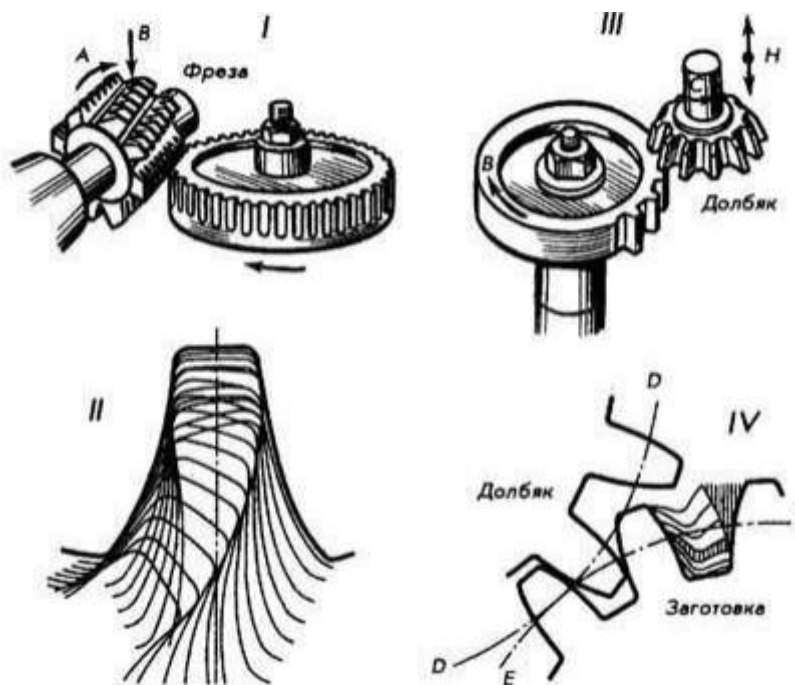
Процесс создания зубчатых колес червячной фрезой, долбяком.
